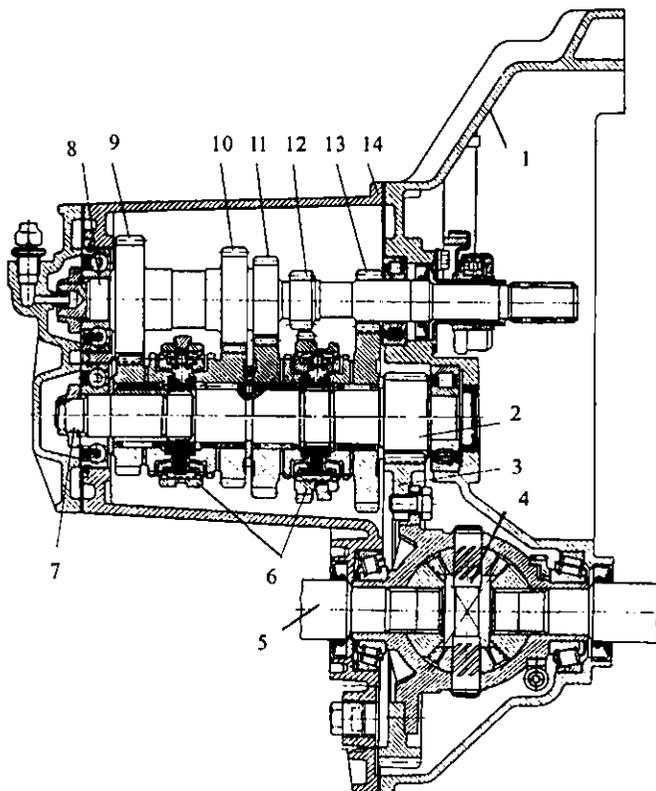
Коробка передач переднеприводного автомобиля ВАЗ-2109:
